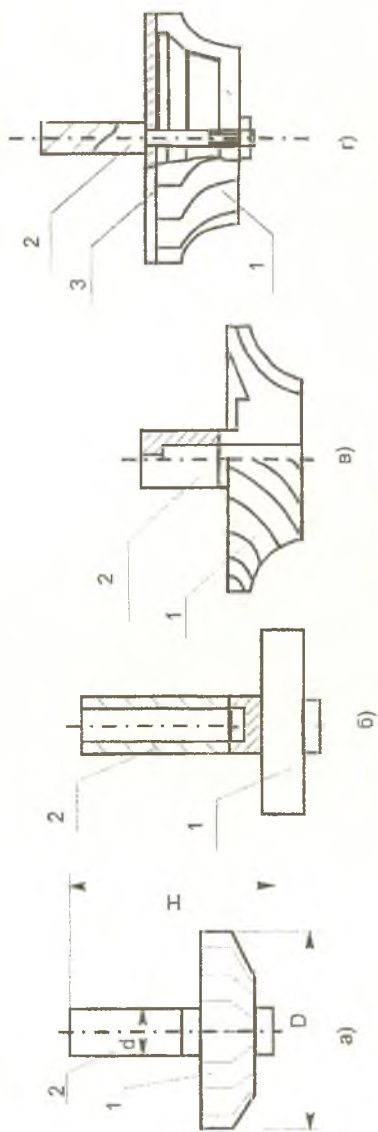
б. Конструкция биметаллических роторов турбин и компрессоров малоразмерных авиационных ГТД, изготавливаемых с помощью диффузионной сварки: а, б - роторы турбин; в - ротор компрессора; г - пустотелый ротор компрессора; 1 - рабочее колесо турбины (ЖС6К, ЖСЗДК, ВЖЛ12У и др.), компрессора (ВТ3-1, ВТ-20 и др.); 2 - вал ротора (Ст.40Х, 45Х, ВНС-2 и др.); 3 - крышка пустотелого ротора компрессора (ВТ-20, В-95 и др.)
